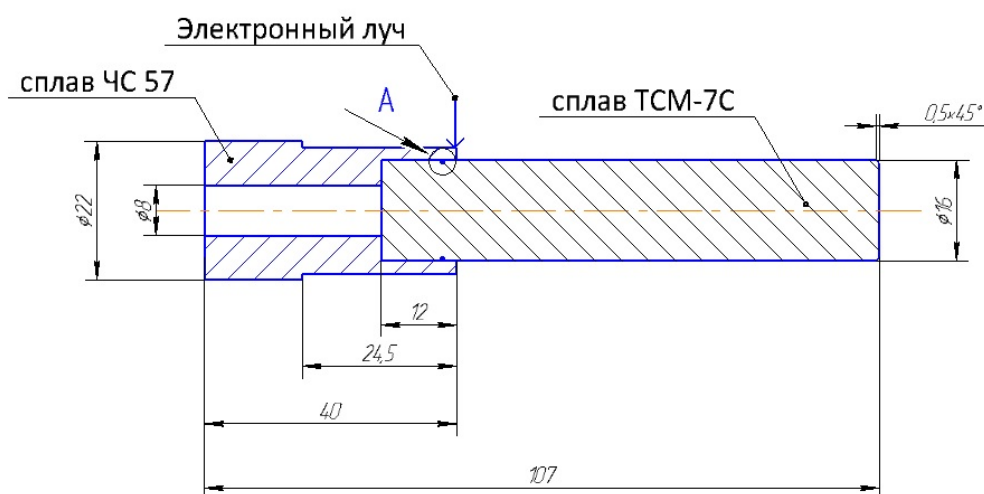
Схема сварко-пайки сплава ТСМ-7С со никелевым сплавом ЧС-57
